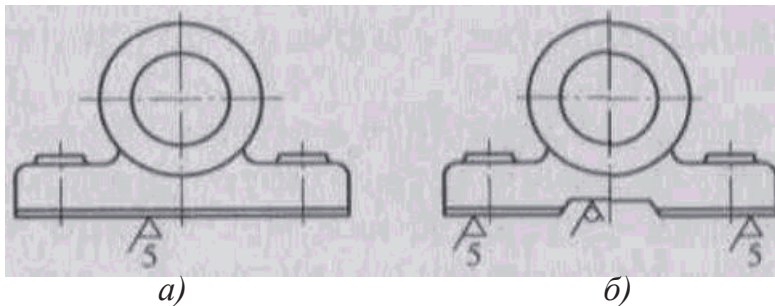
Два исполнения установочной базовой поверхности корпуса: *a* – нетехнологичное; *б* – технологичное
